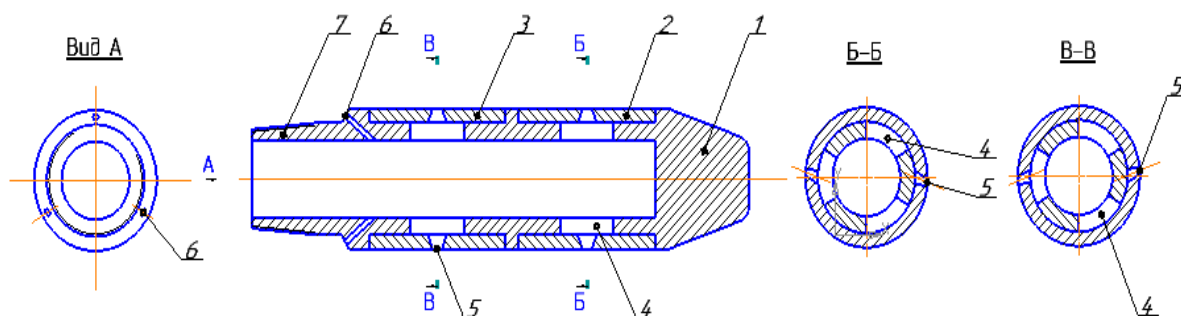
Чертеж гидромониторной роторной насадки, здесь 1 – корпус, 2 – передний ротор, 3 – задний ротор, 4 – прорези, 5 – сопло, 6 – реактивное сопло, 7 – резьба.
